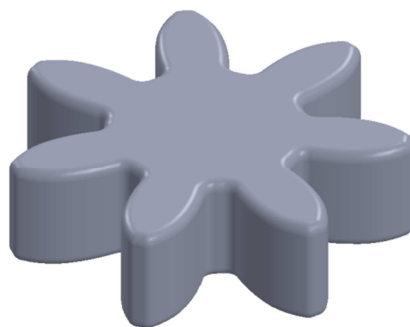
Modelo CAD del engranaje de módulo 4 y 7 dientes.
